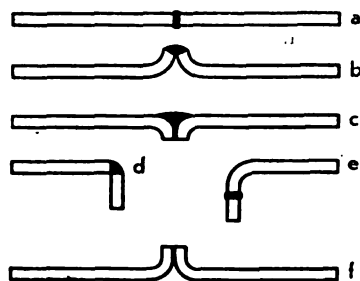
Ausführungsarten von Stumpfnähten bei Dünnblechschweißungen.
